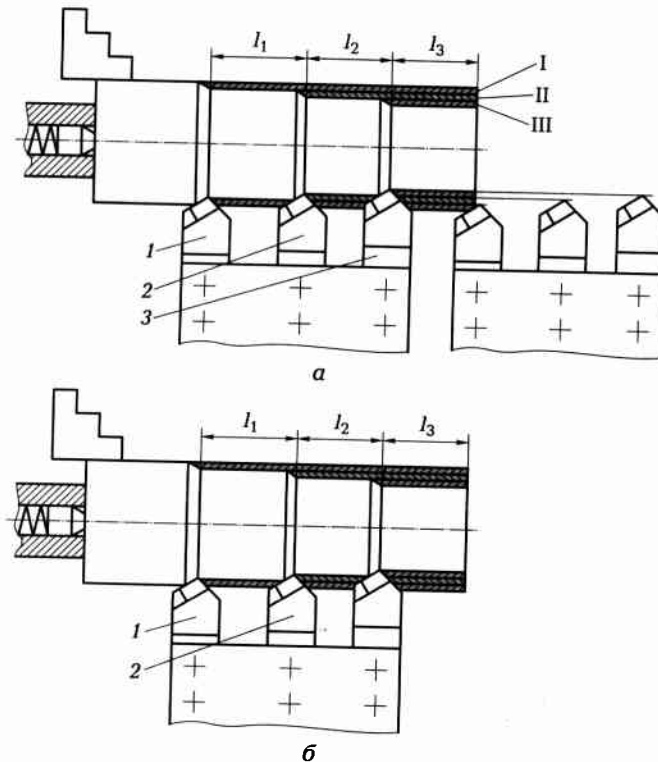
Схемы наладки многорезцового станка при обработке вала (а, б)
